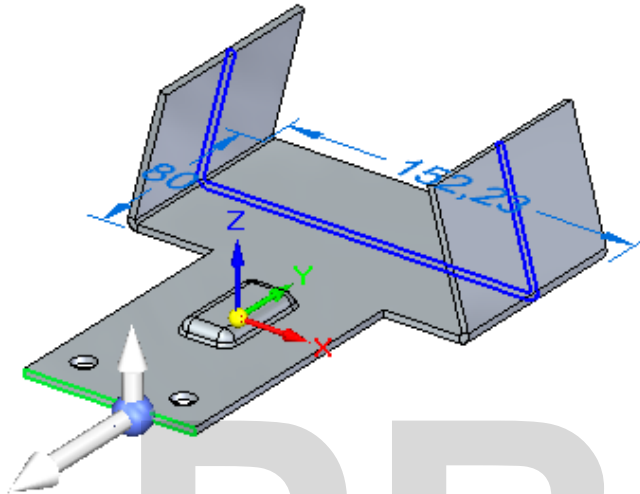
Flächenwerkzeug und Lappengriff bei Auswahl einer planaren Blechkante (Stärkefläche)
